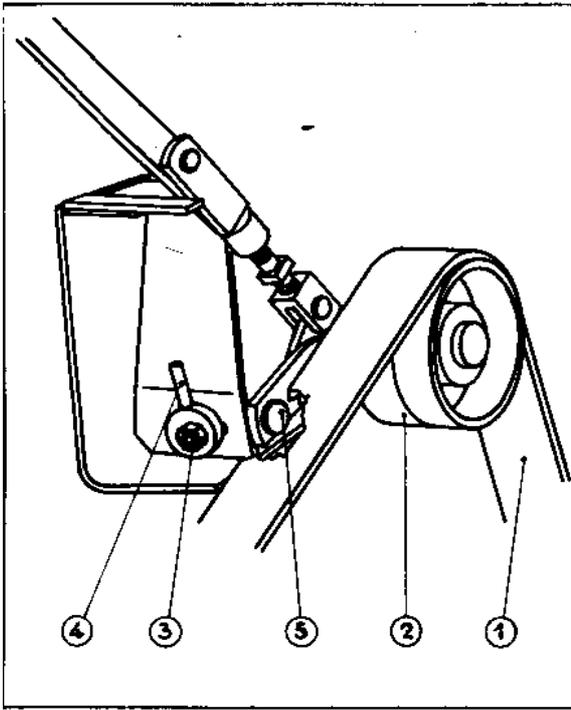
Réglage du galet tendeur de courroie d'embrayage batteuse -
